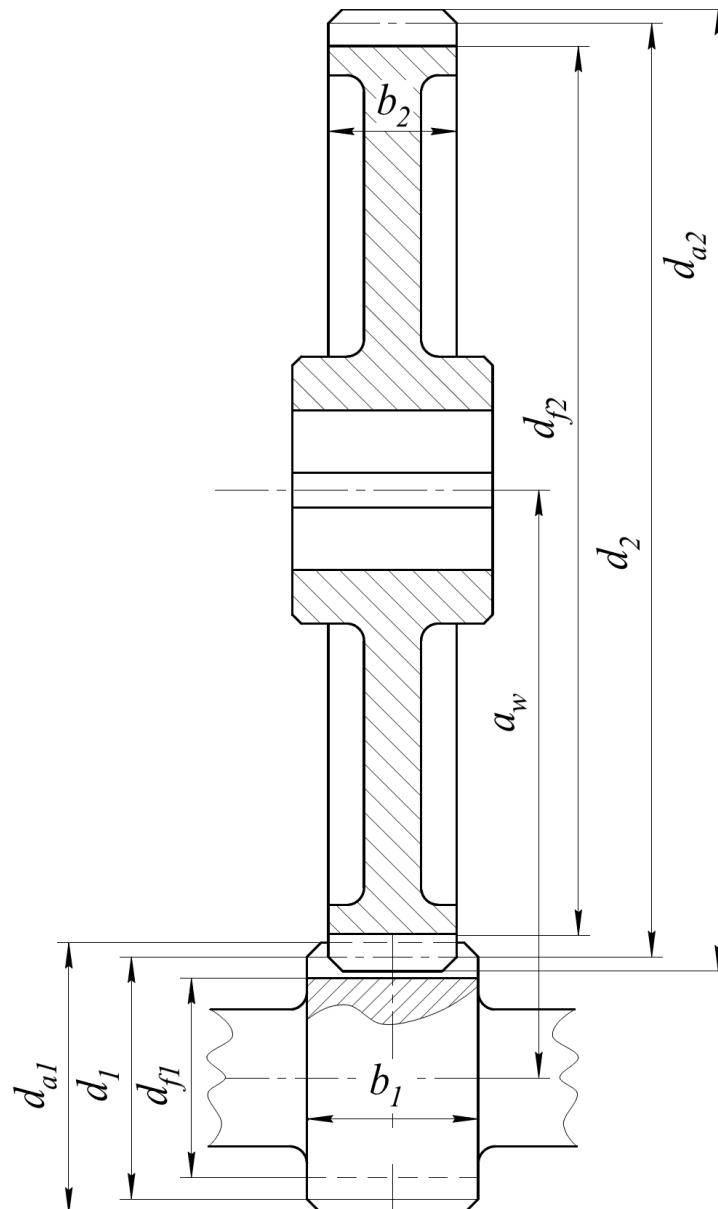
Ескіз зубчастої циліндричної передачі
